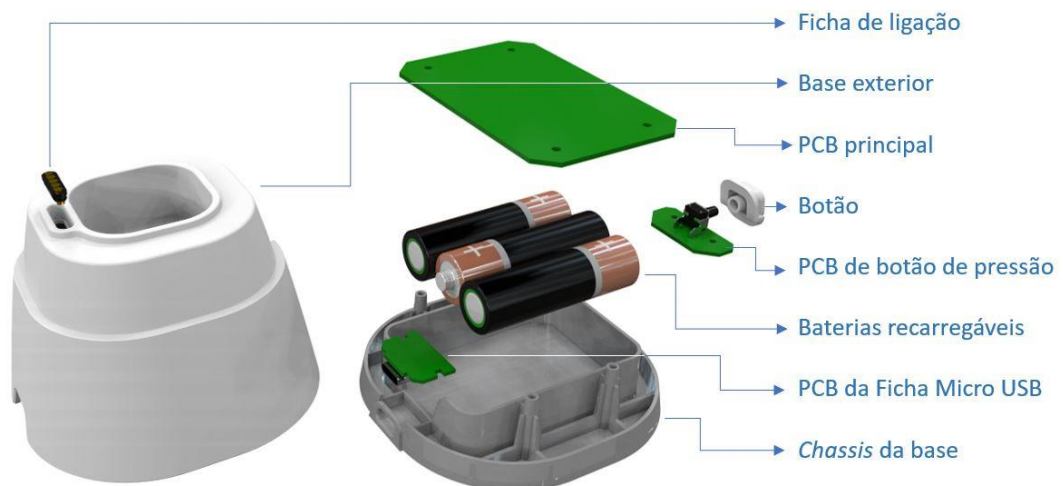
Vista explodida dos componentes principais da base do dispositivo de difusão
